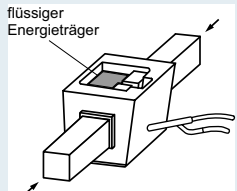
Wirkpaarungen beim Schweißen
